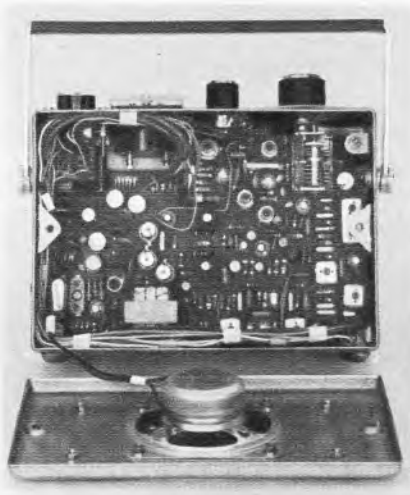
Innenansicht vom 2-m-Funksprechgerät
